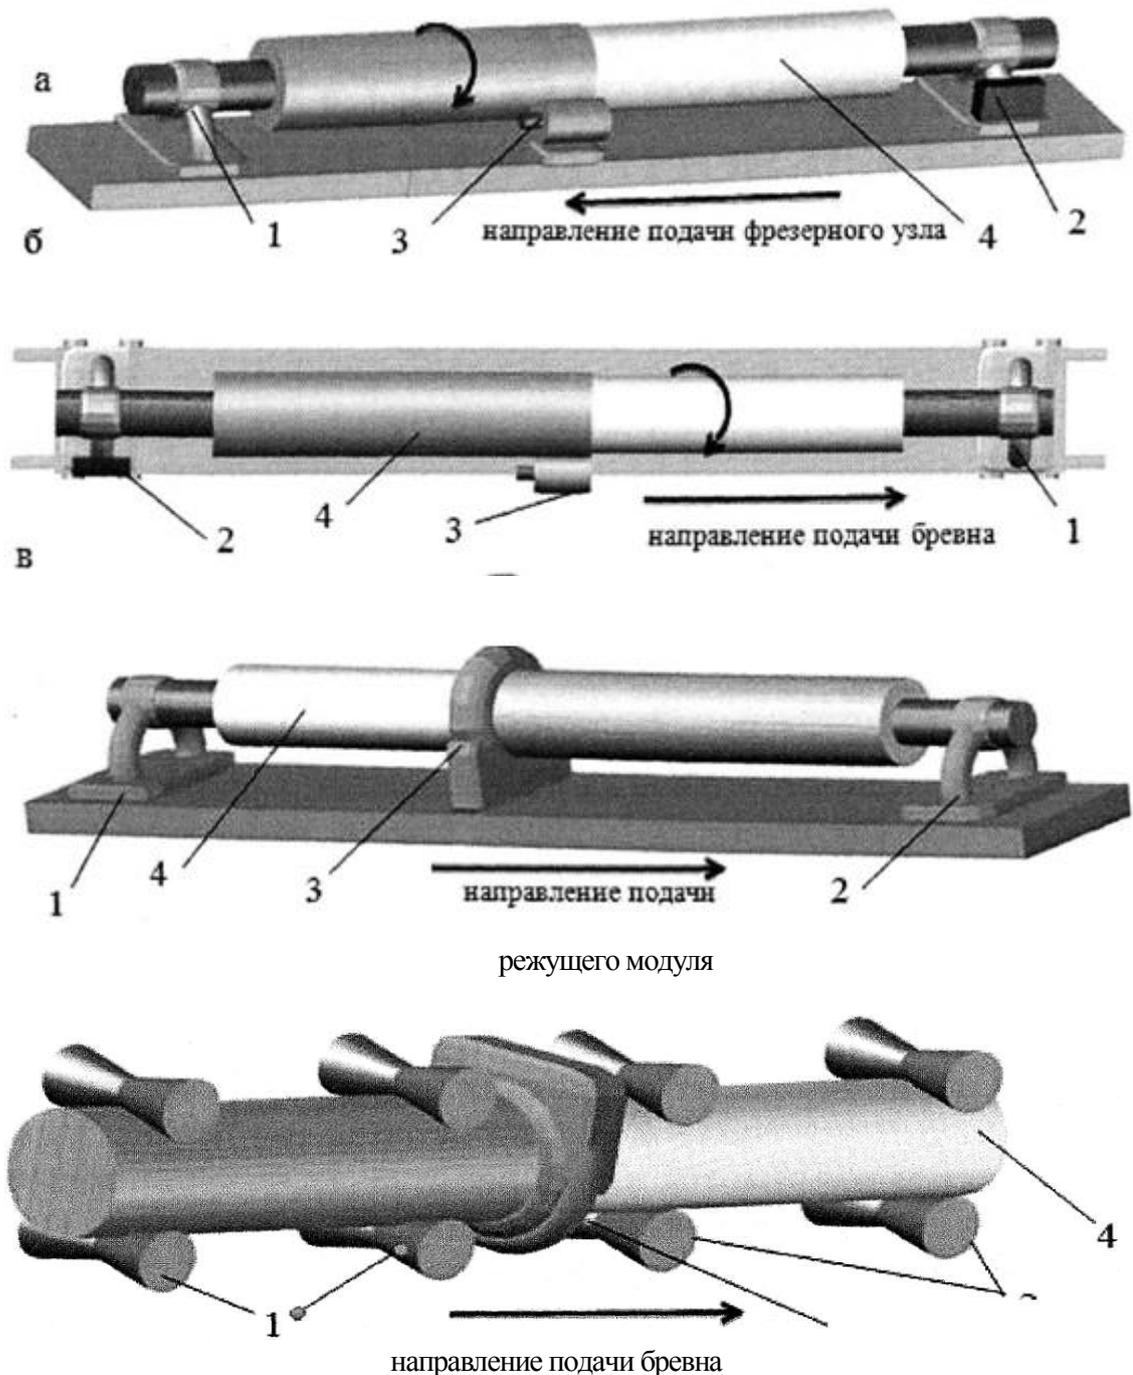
Принципиальные схемы станков для производства оцилиндрованных деталей строительного назначения. Станки периодического действия: а - центрального типа с вращающимся бревном и подвижным фрезерным узлом: 1 - подвижная зажимная бабка; 2 - зажимная бабка с приводом вращения бревна; 3 - подвижный фрезерный узел; 4 - обрабатываемое бревно; б - центрального типа с надвиганием вращающегося бревна на стационарный фрезерный узел: 1 - подвижная зажимная бабка; 2 - зажимная бабка с приводом вращения бревна; 3 — стационарный фрезерный узел; 4 — обрабатываемое бревно; в — центрального типа с неподвижным бревном: 1, 2 — зажимные бабки; 2 - подвижной режущий модуль; 4 - обрабатываемое бревно. Станки проходного типа: г — 1 — подающие вальцы; 2 — приемные вальцы; 3 - стационарный режущий модуль; 4 - обрабатываемое бревно
